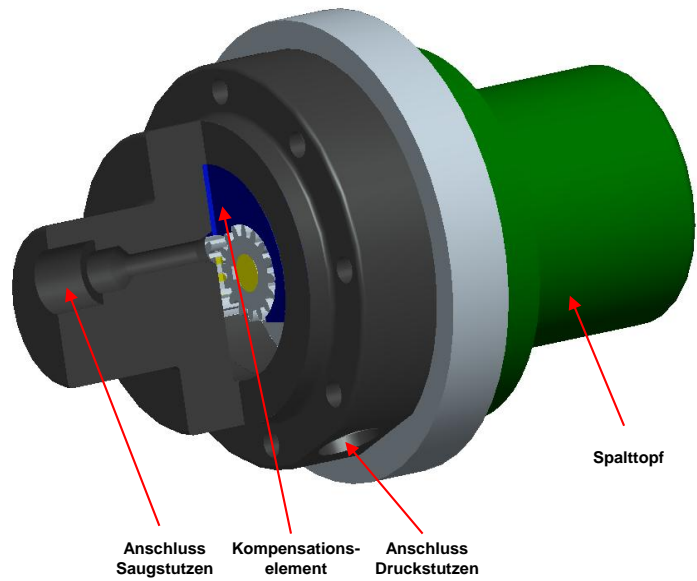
3D-Schnitt durch die Prototypenpumpe
